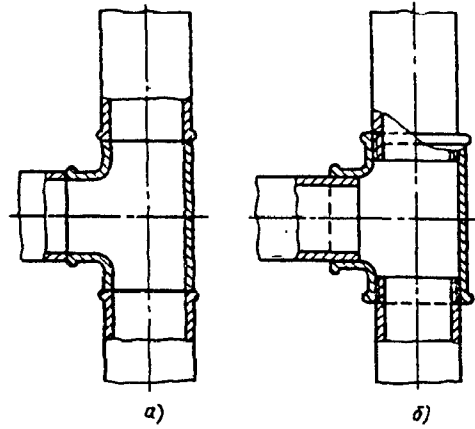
Схема кольцевого выступа в стандартном тройнике: а—сварной тройник; б—соединение труб в тройнике на резьбе
